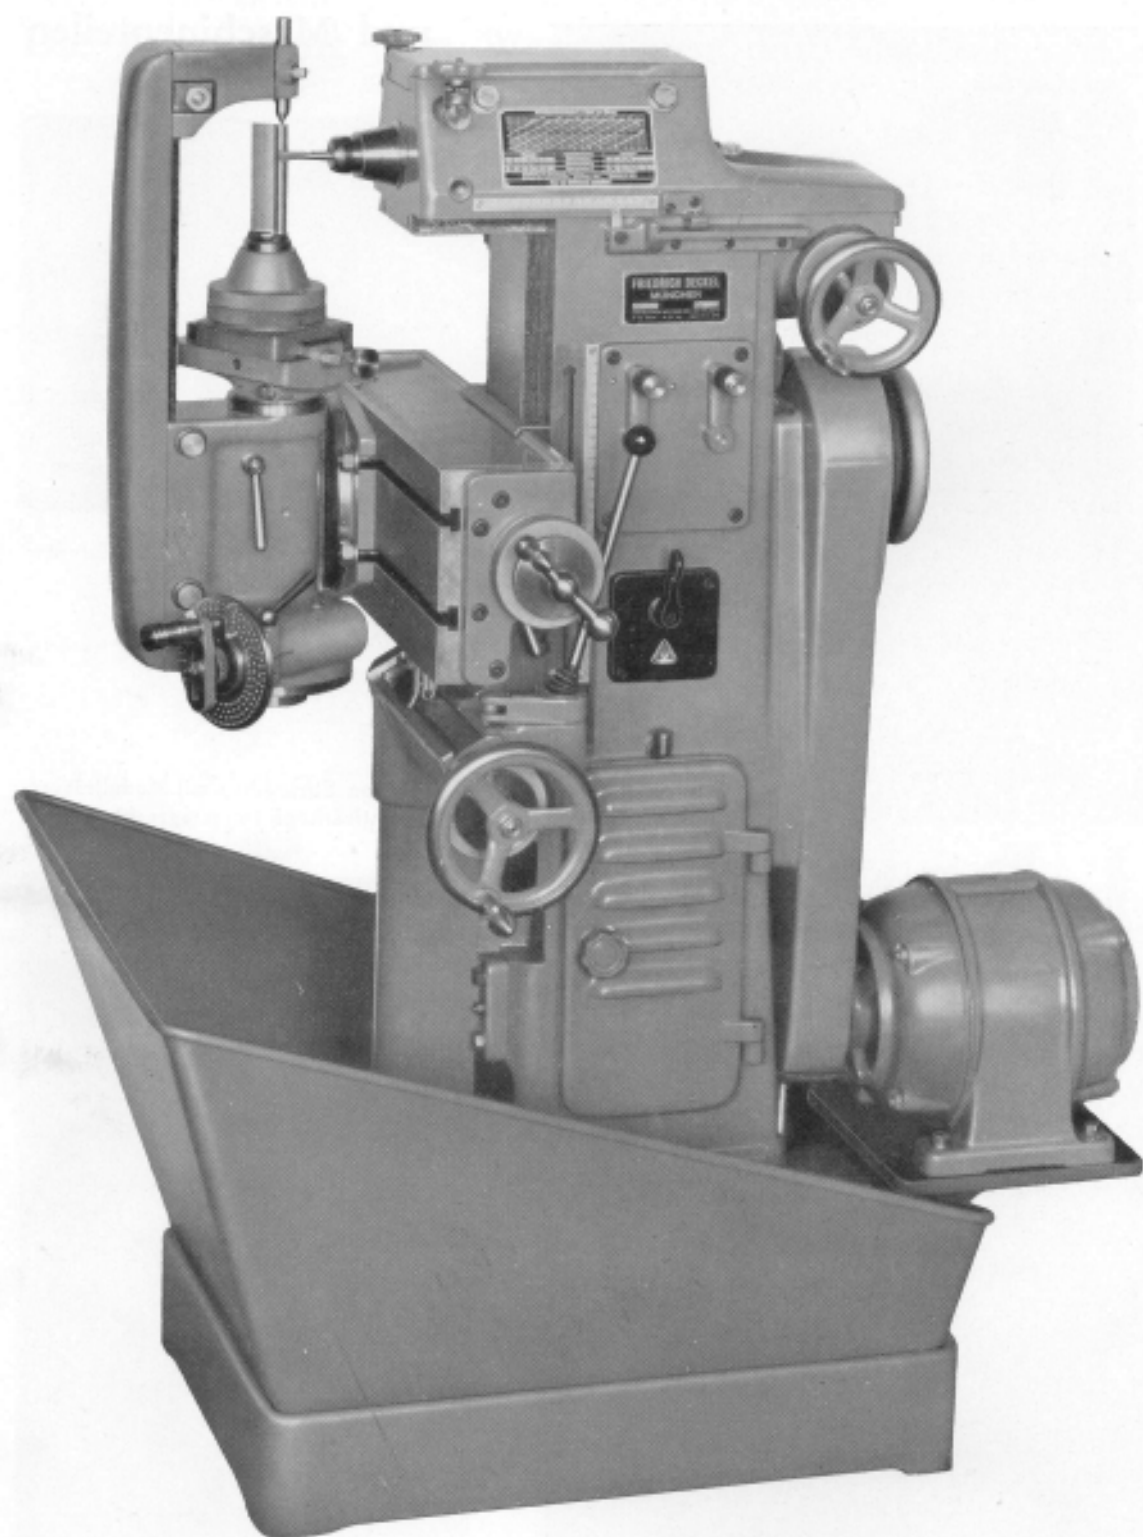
FP 1 Maschine eingerichtet für das Stempelfräsen
